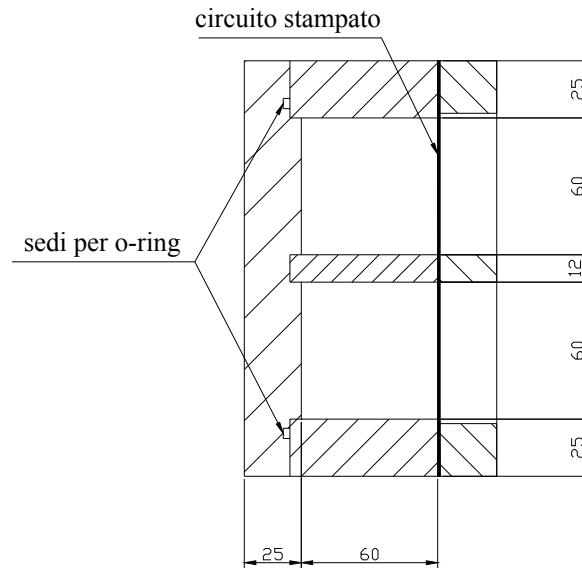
Sezione retta del canale nella sezione di prova.
